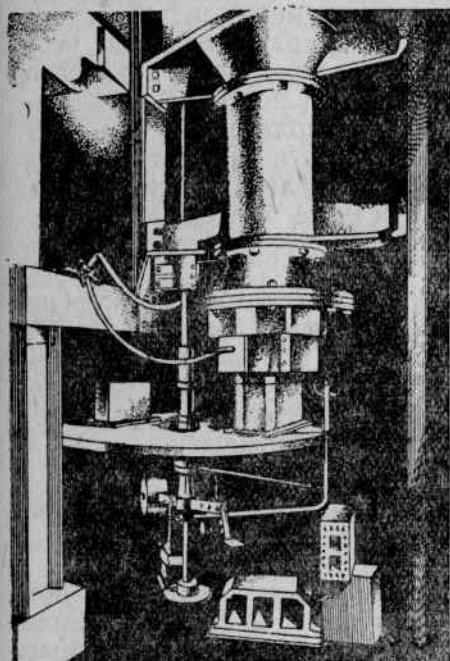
Вертикальный пресс с поворотным столиком для формовки блоков.
